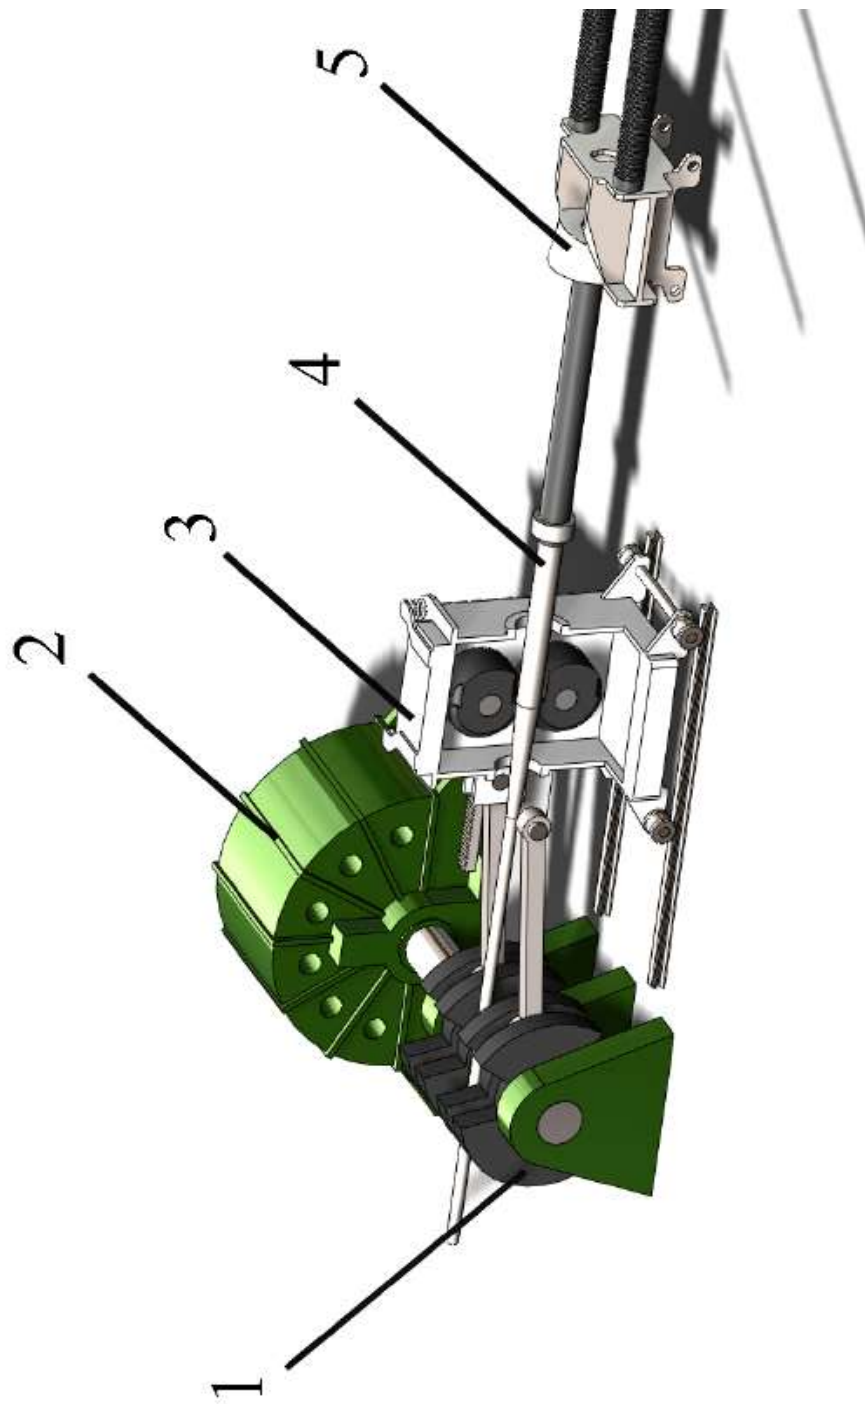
Стан холодной прокатки труб: 1 – кривошипно-шатунный механизм; 2 – двигатель; 3 – прокатная клеть; 4 – трубная заготовка; 5 – вспомогательный механизм
